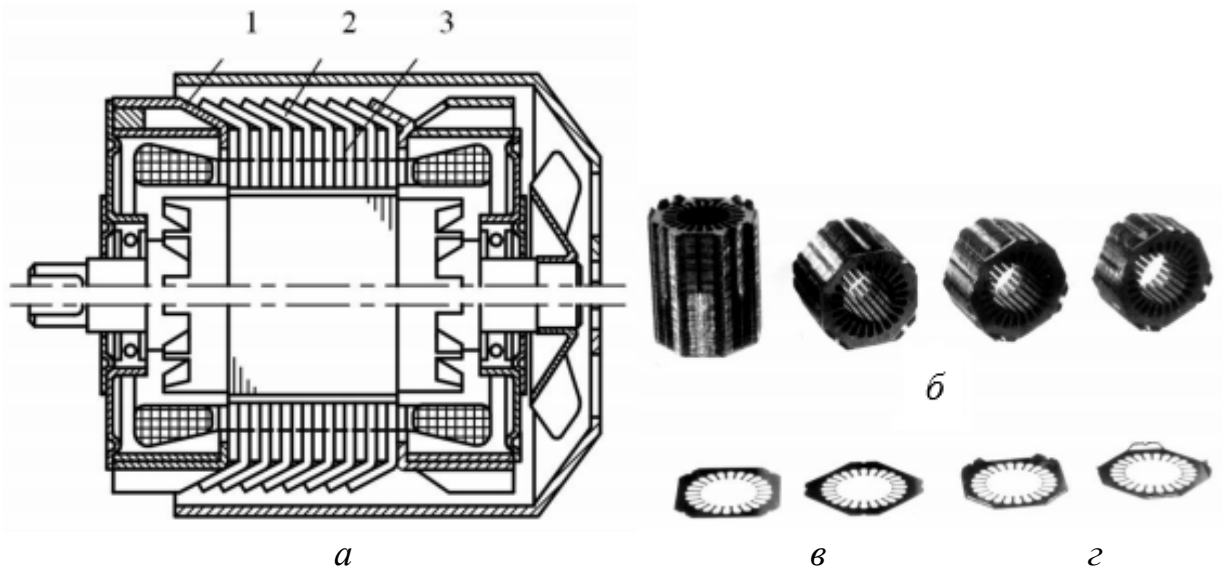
Конструктивна схема (а) і особливості багатоплощинного магнітопроводу (б-г) асинхронного двигуна: 1 – опорний елемент; 2 – опорна ділянка ярма; 3 – зубцово-пазовий шар з плоскими та багатоплощинними ділянками електротехнічної сталі.
